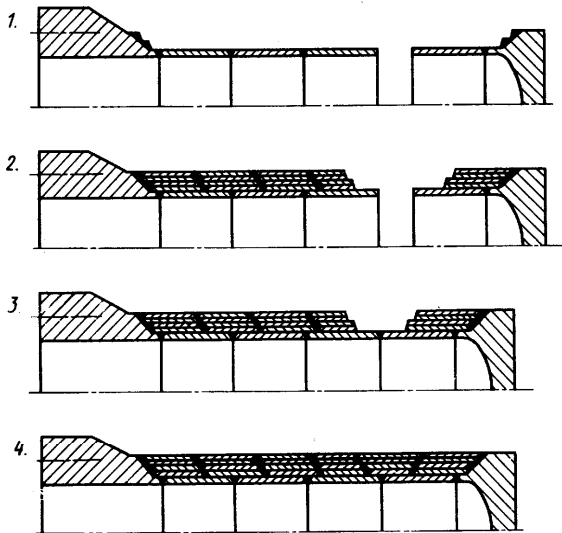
Технологическая последовательность (1...4) изготовления сосуда со смещенными сварными швами
